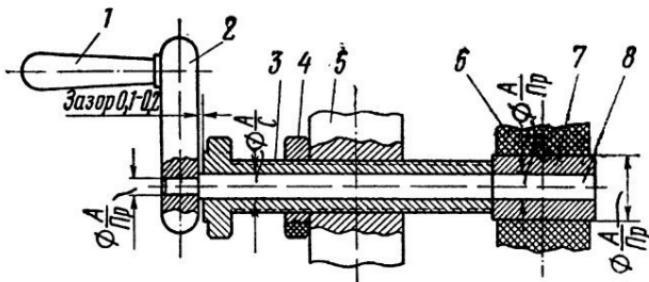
Модель бесступенчатого вариатора скоростей (схема соединения деталей привода): 1 — ручка; 2 — рычаг ручки; 3 — втулка-регулятор; 4 — контргайка; 5 — кронштейн; 6 — ведущий диск; 7 — металлическая втулка; 8 — вал привода.
